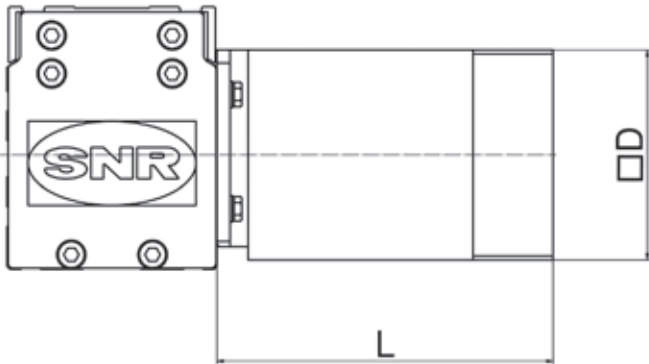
Abmessungen AXC mit steckbarem Planetengetriebe Variante ZS und ZT
